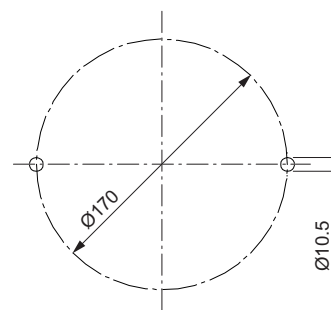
Схема сверления для клапанов из нержавеющей стали
